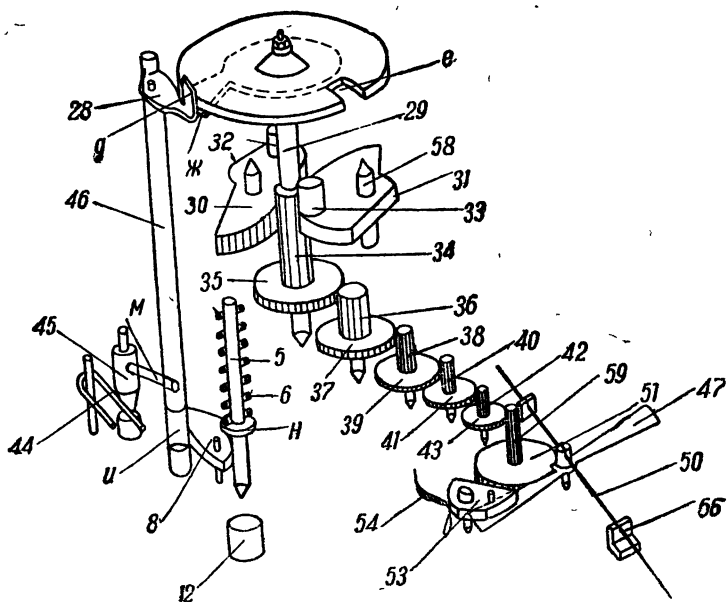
Схема дистанционного механизма со спусковым приспособлением взрывателя М43 А2 (пояснение деталей см. рис. 65).
